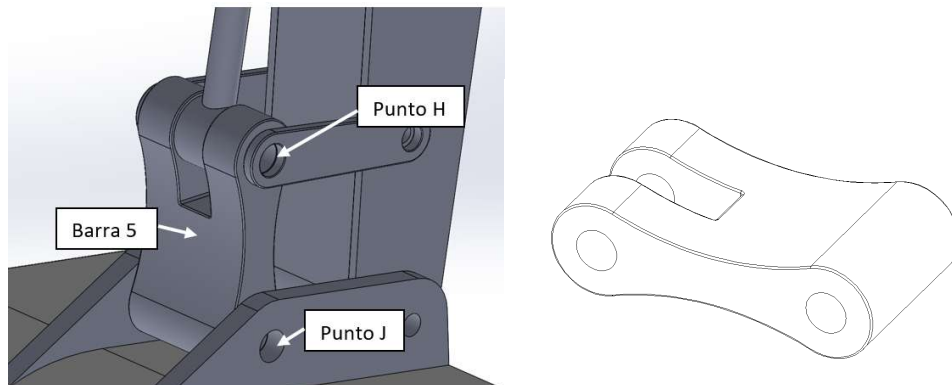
Barra 5 en el ensamblaje de SolidWorks
